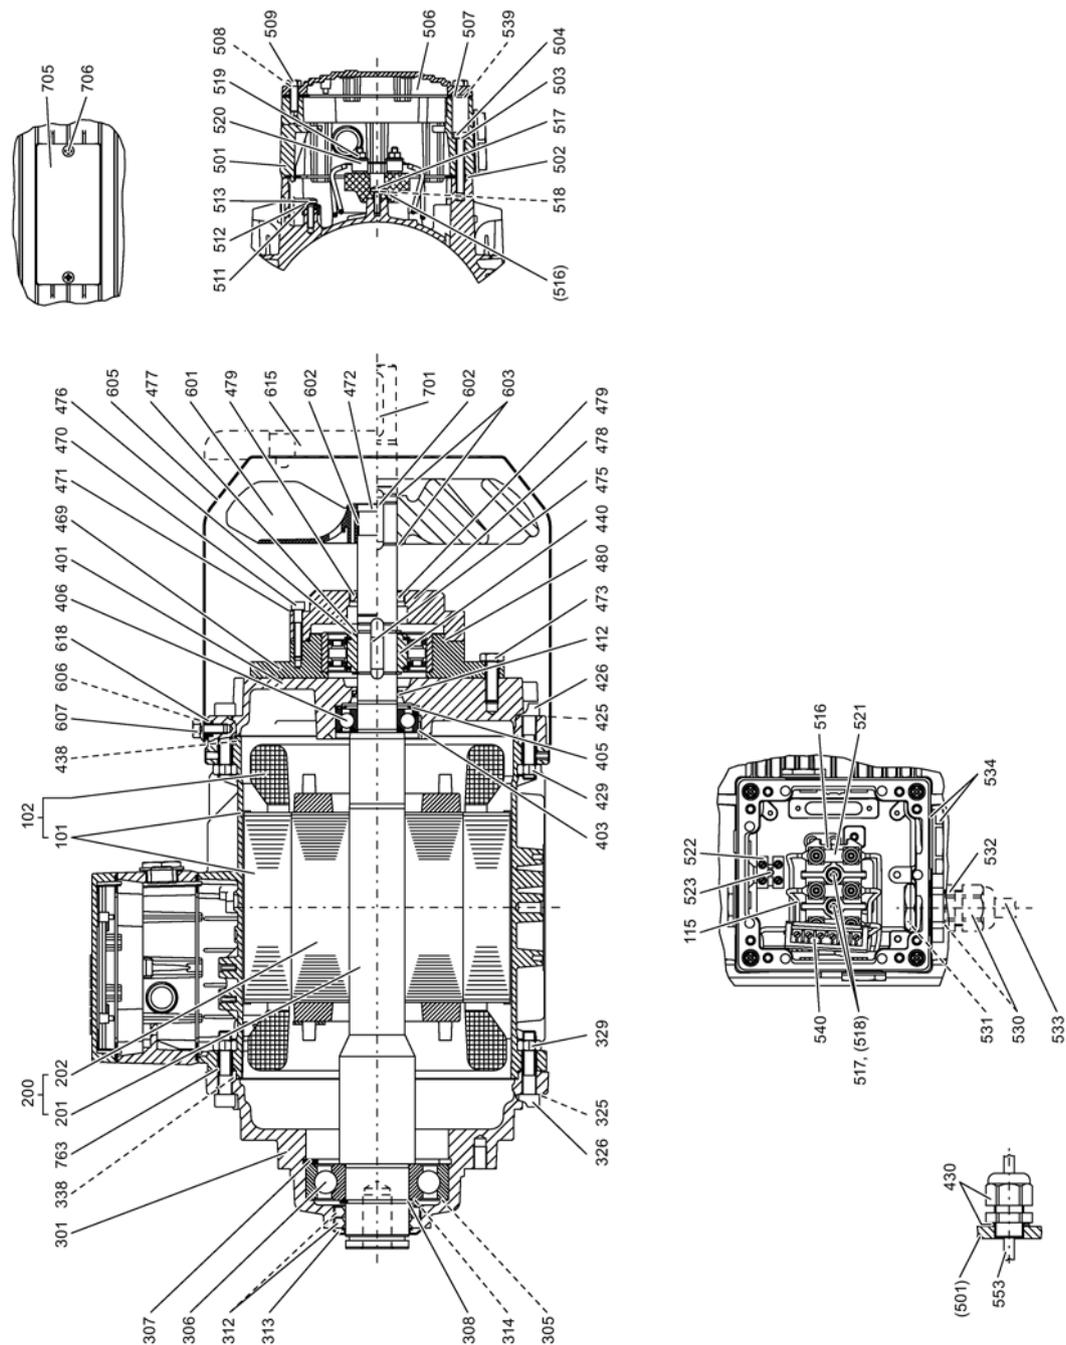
MODULOG Motor Baugrößen LA100 - LA160 mit Rücklaufperre
